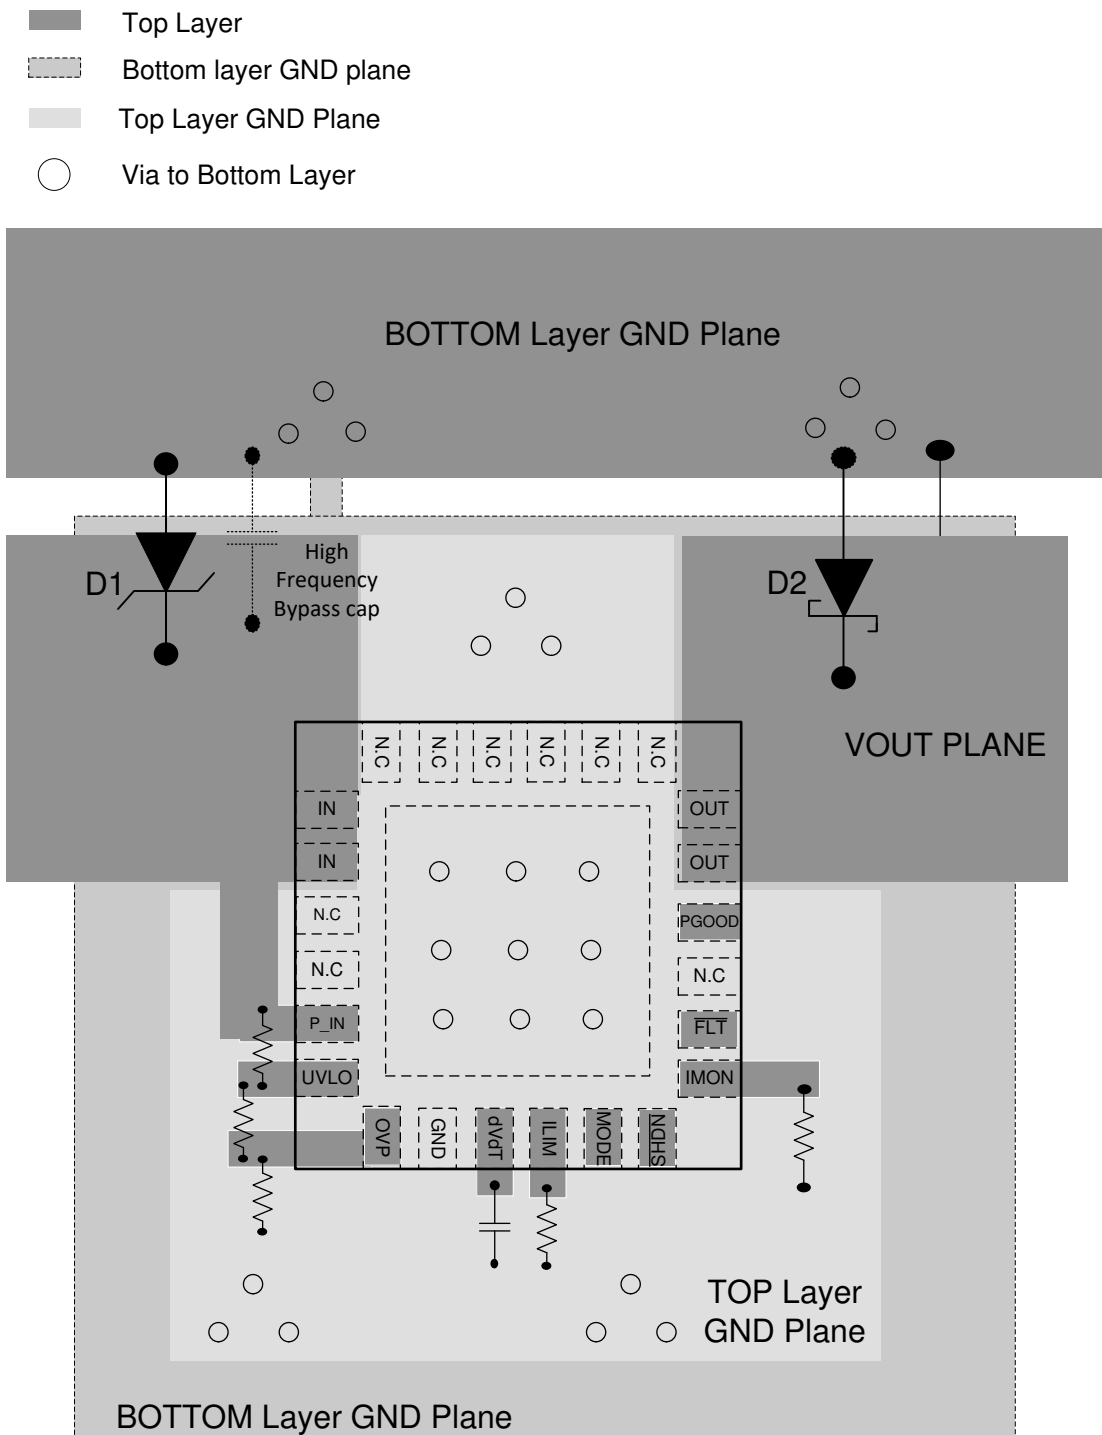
采用 QFN 封装并采用 2 层 PCB 的 PCB 布局示例
